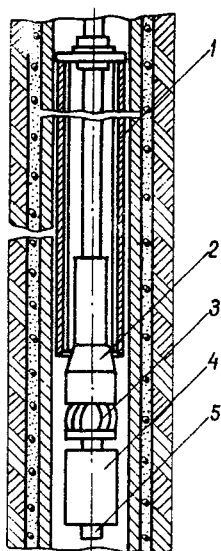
Устройство для установки металлических гофрированных пластырей "Дори": 1-гофрированный пластырь; 2-конус-пуансон; 3-толкатель; 4-обратный клапан.
